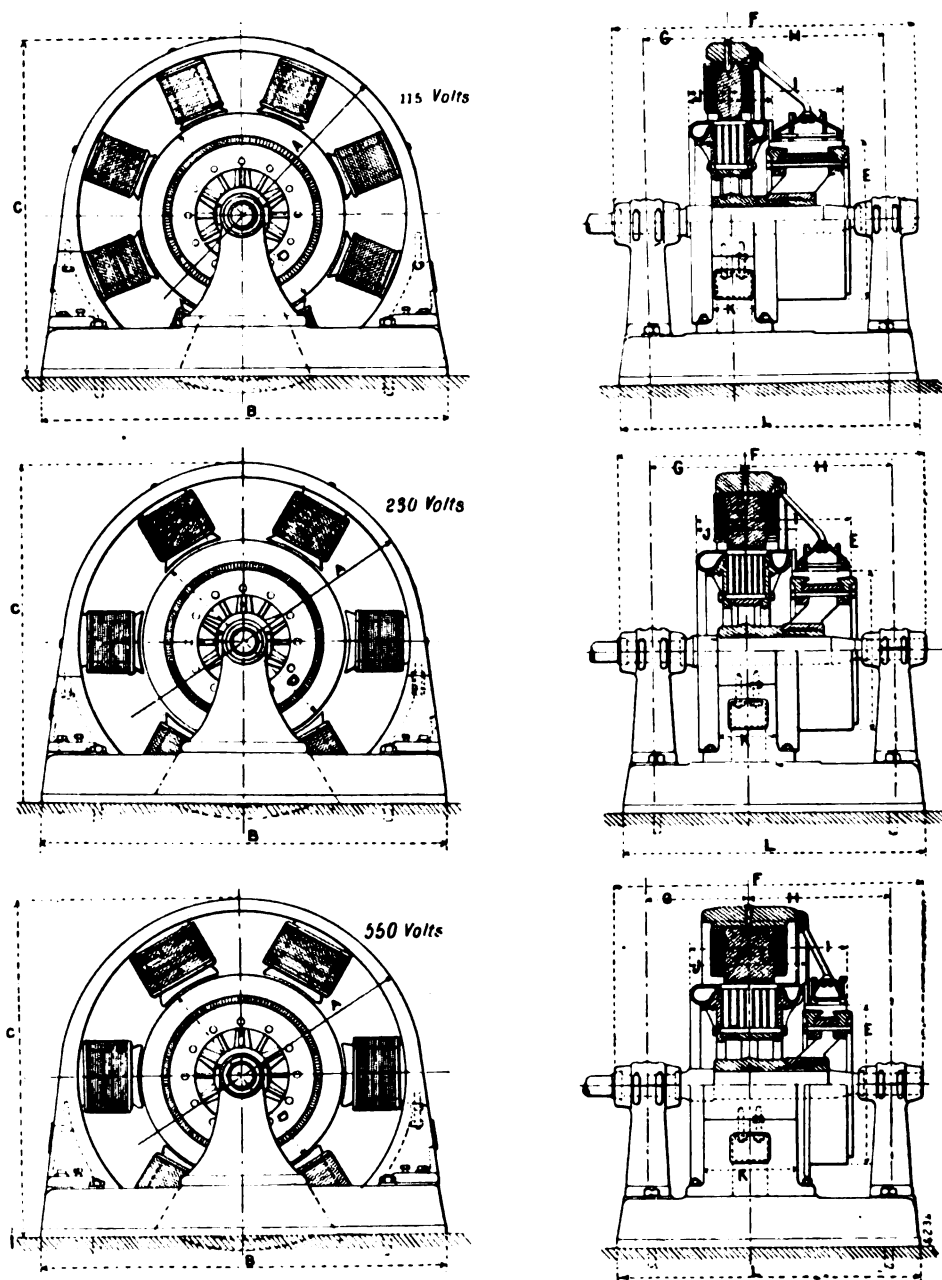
Vue de côté et coupe des 3 machines de 100 kilowatts.
